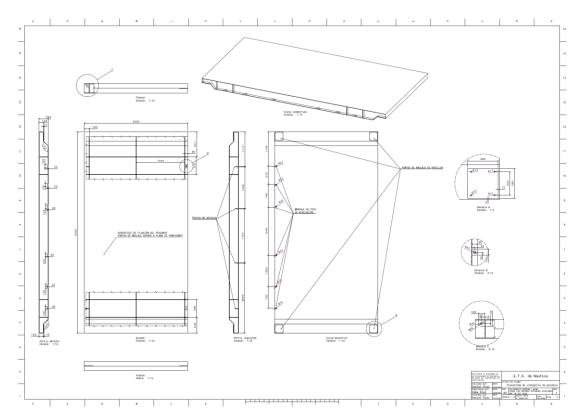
Plano de estructura portante. 2025. Elaboración propia.
